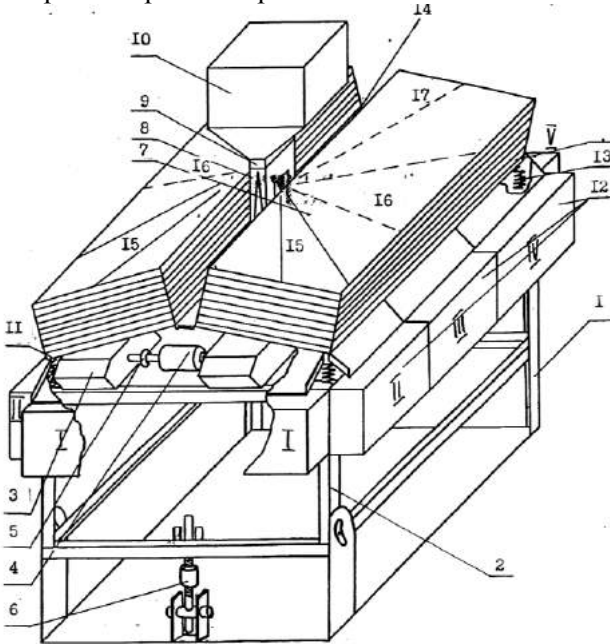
Конструктивна схема віброфрикційного сепаратора:
